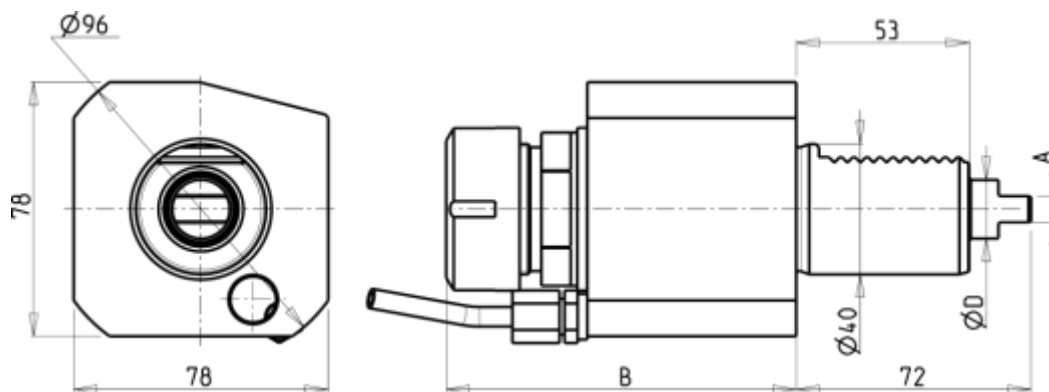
Размеры сверлильно-фрезерной головки DA40180932
